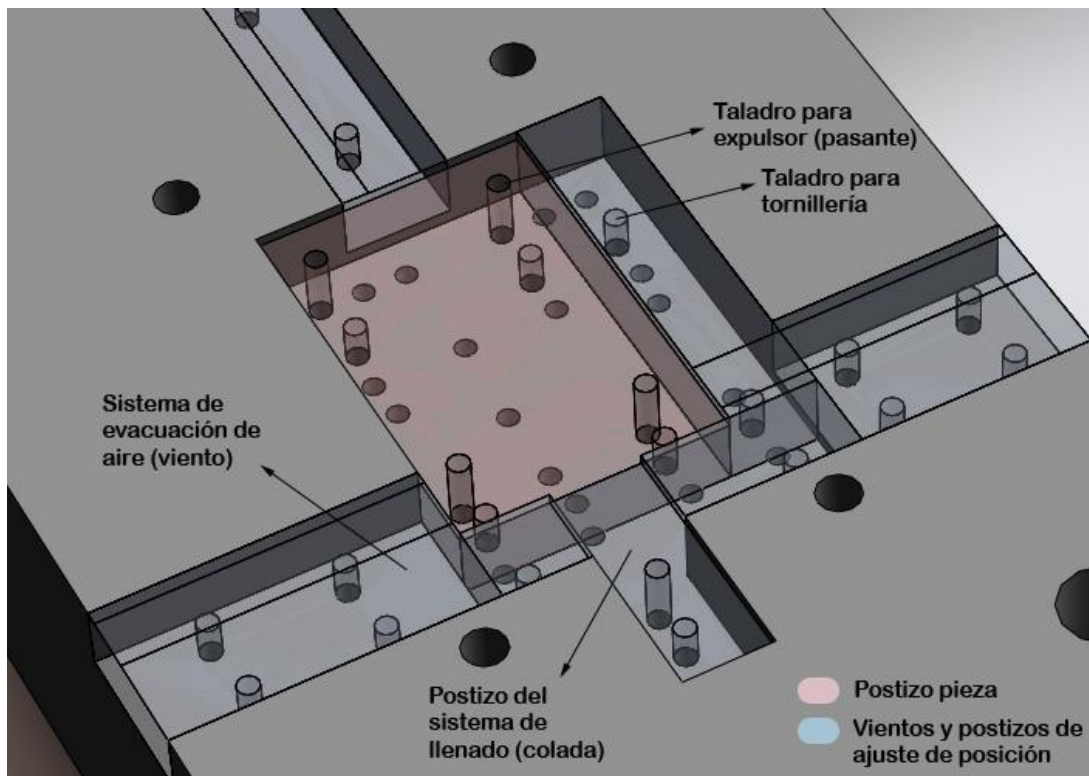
Detalle transparente de la configuración de llenado central largo.
